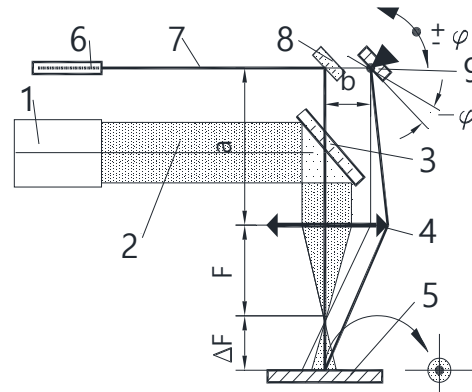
Схема оптичної системи лазерної установки з використанням методу подвійного зображення для налаштування відносного положення об’єктиву та поверхні заготовки (1 – лазер ЛУ, 2 – робочий промінь, 3 – поворотне дзеркало, 4 – об’єктив, 5 – заготовка, 6 – лазер додатковий, 7 – промінь додаткового лазера, 8, 9 – дзеркала подільника променя 7)
